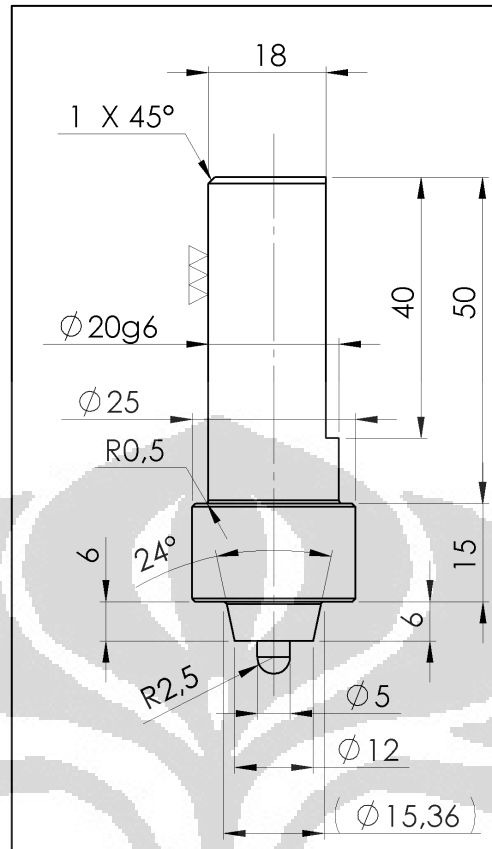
Tool FSW dengan Cyl probe $\varnothing 5$ mm
